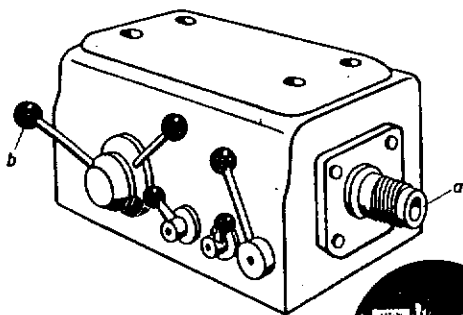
Cabezal fijo: a) husillo principal; b) palanca de embrague.
